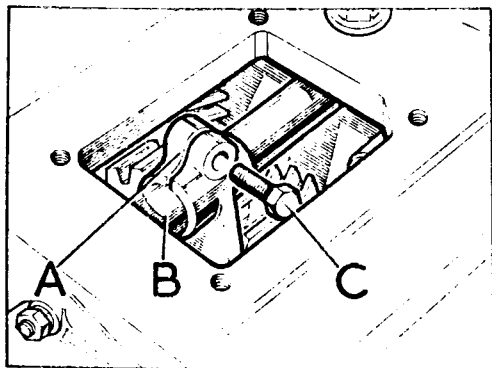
Conjunto de la horquilla selector de la caja reductora
